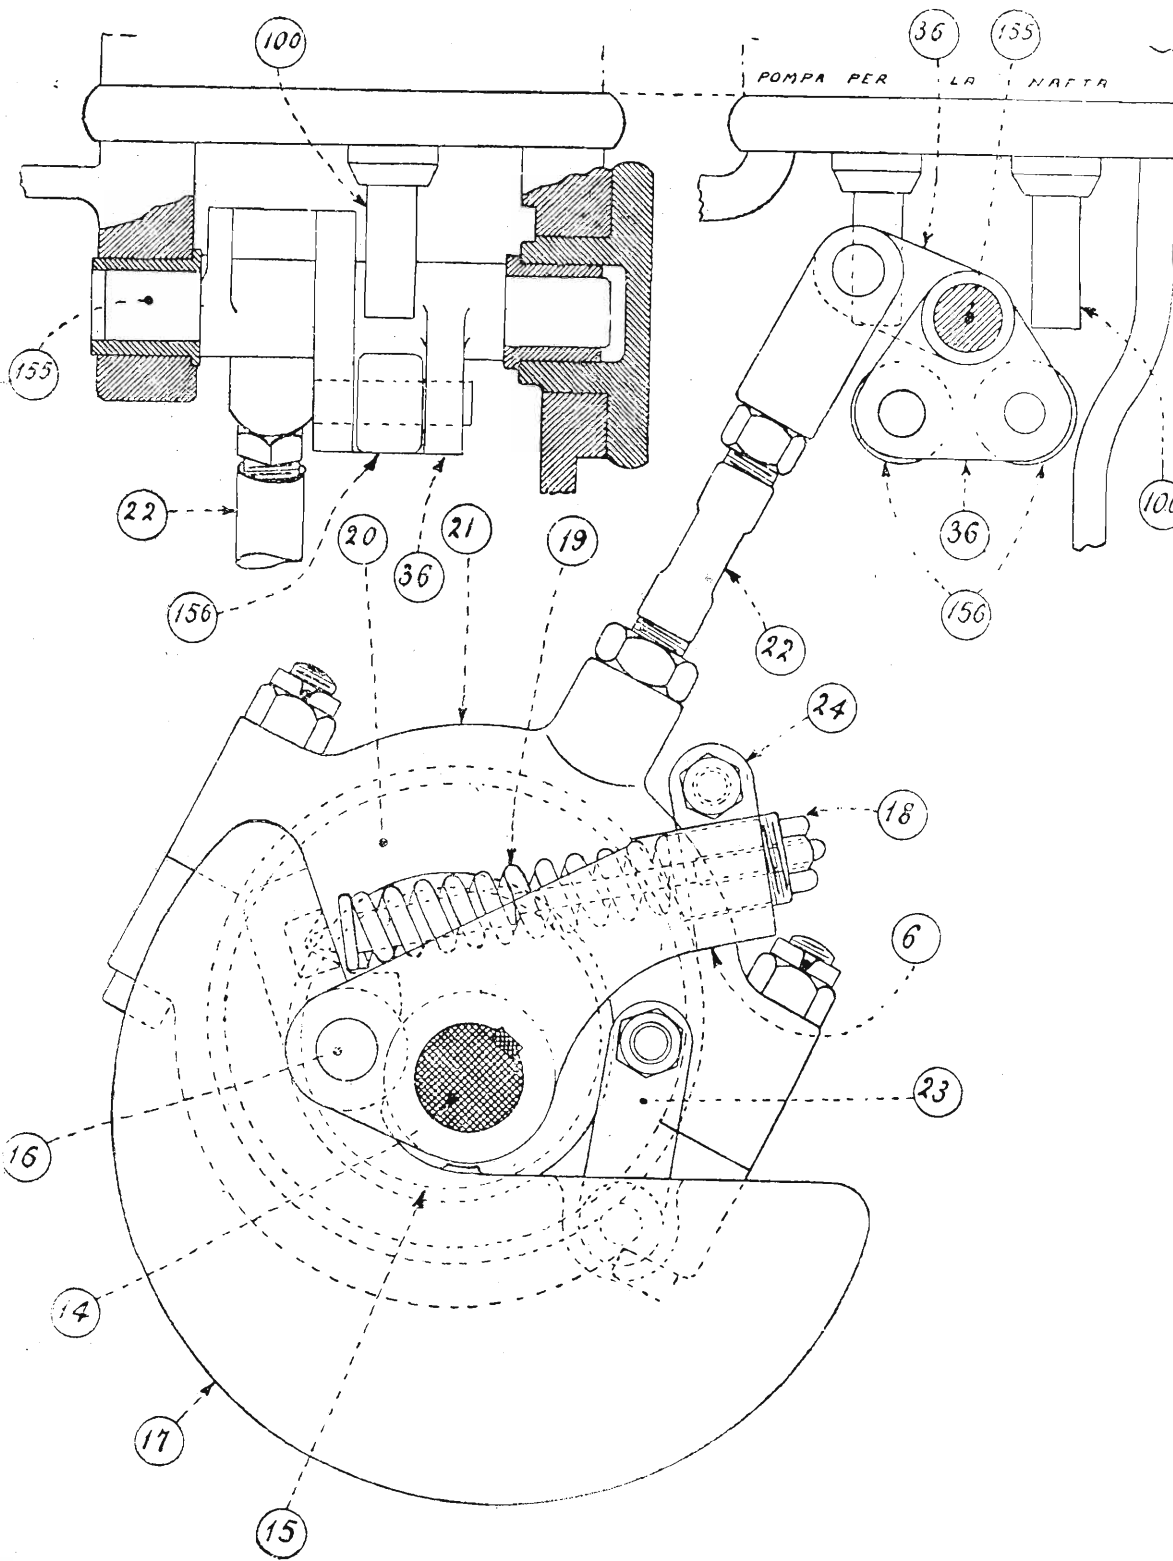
Motore a testa calda S. Giorgio da 18 KW.
